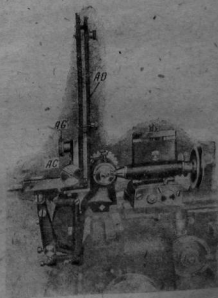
Станок Петерман для фрезеровки торцовых зубьев. Делительное устройство и шпиндель.
